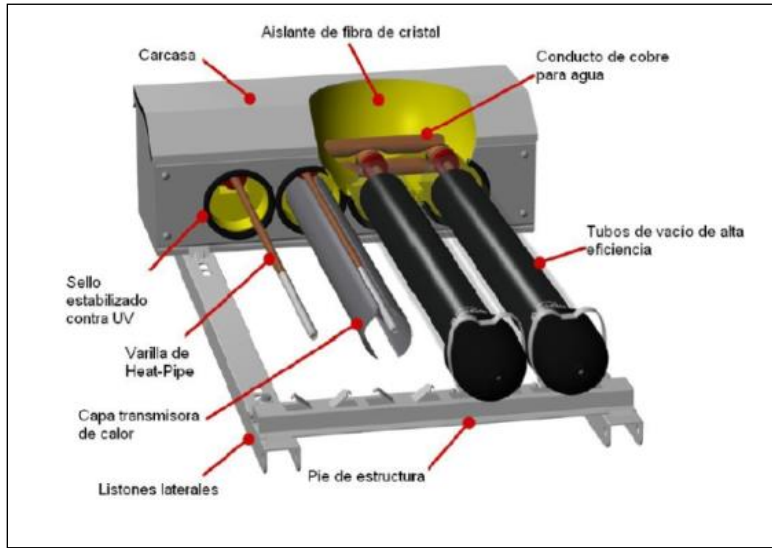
Componentes de un colector de tubos heat pipe. Fuente sogaltecsolar.com
